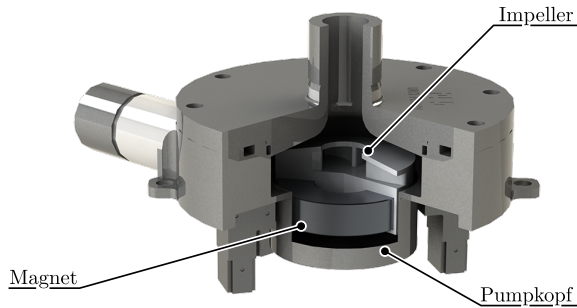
Schnittzeichnung des Pumpkopfs und des Impellers.
